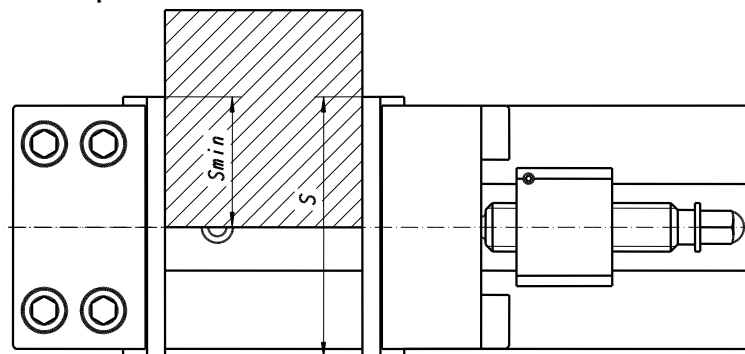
Spannen des Werkstücks mit irregulärer Form.
